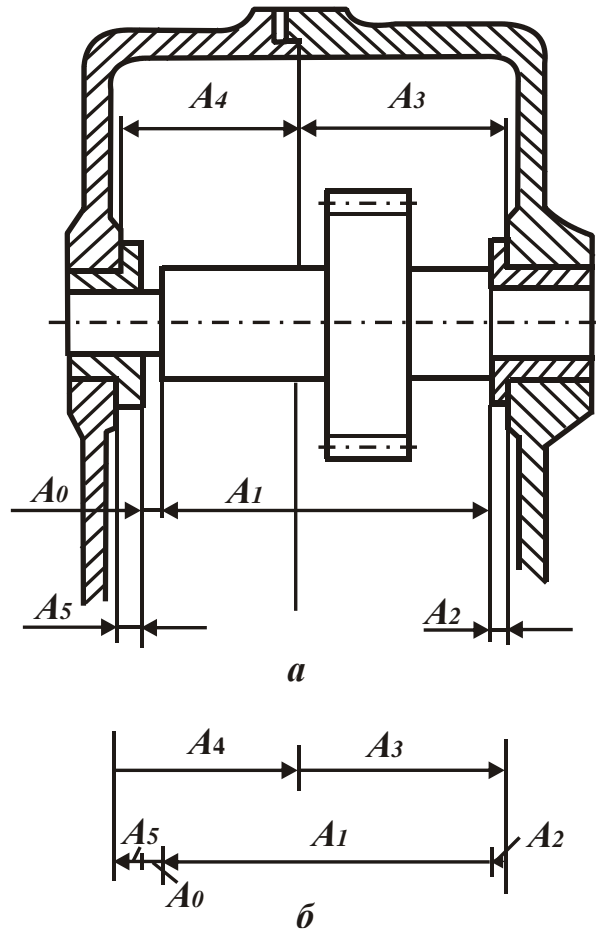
Лінійні розміри роз'ємного корпусу зубчастої передачі
